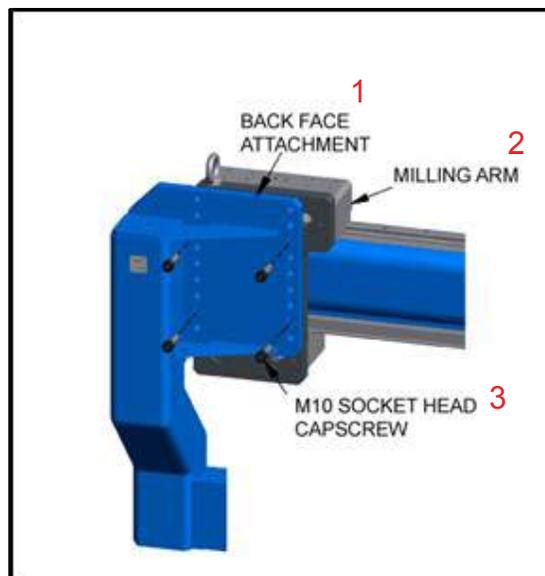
DÉTAIL DE L'ASSEMBLAGE DE LA FIXATION ARRIÈRE
